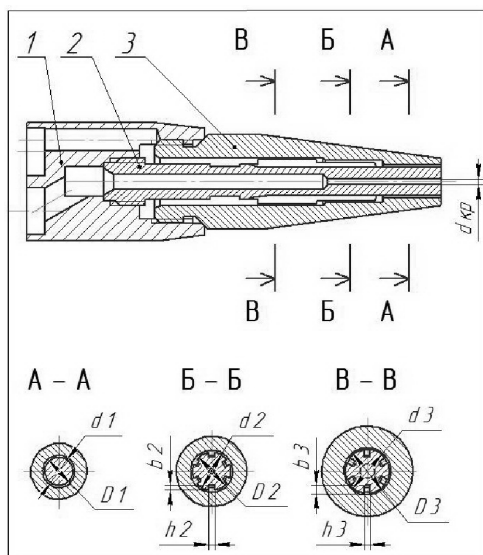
Модуль 6.1. Головка резака Р1ШСп для вырезки корня сварного шва и снятия фасок под сварку
